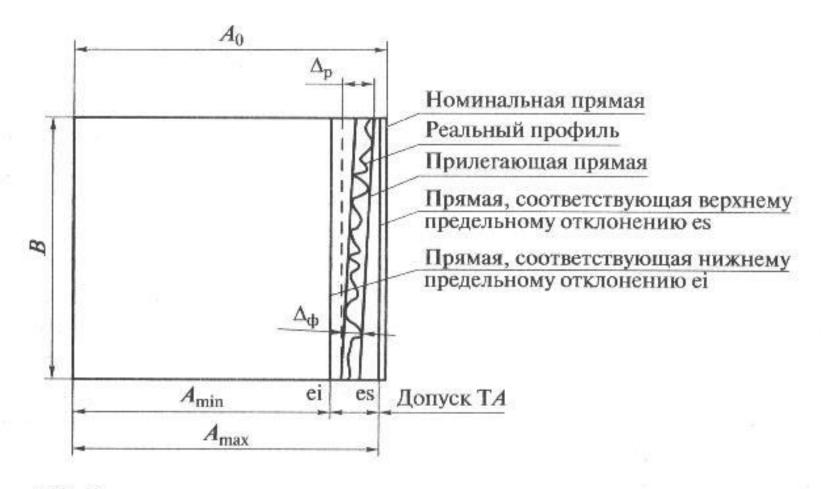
Геометрическое представление допуска номинального размера, формы и расположения в сечении плоской детали
